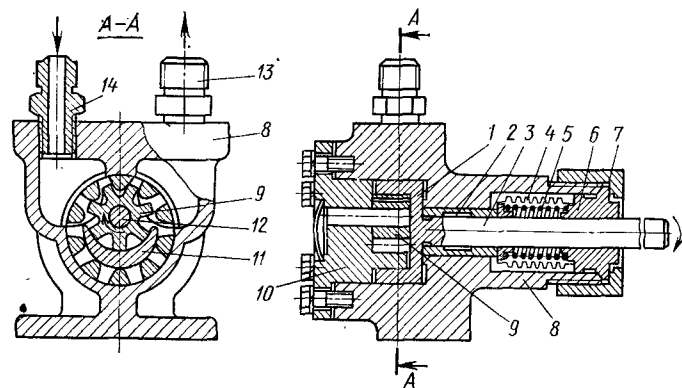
Шестеренчатый топливоподкачивающий насос:
